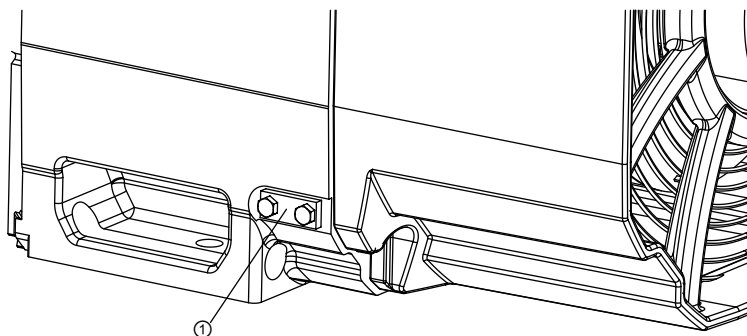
Клеммная планка ① для заземляющего провода для двигателя с принудительным охлаждением
